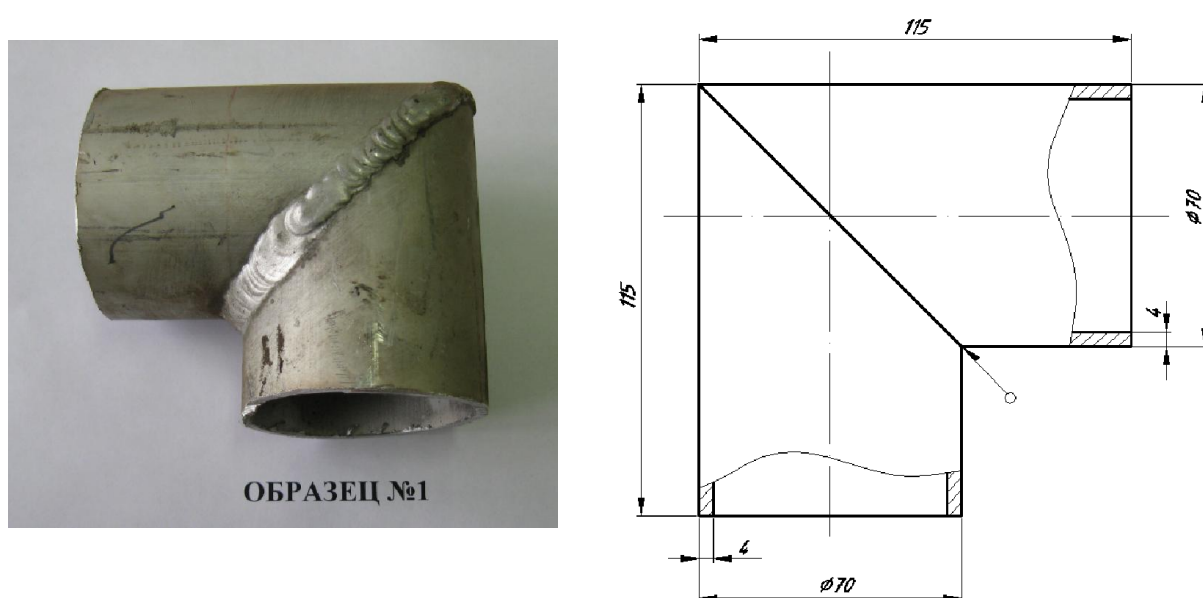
Образец №1 («угольник») для исследования остаточных напряжений в сварном шве
